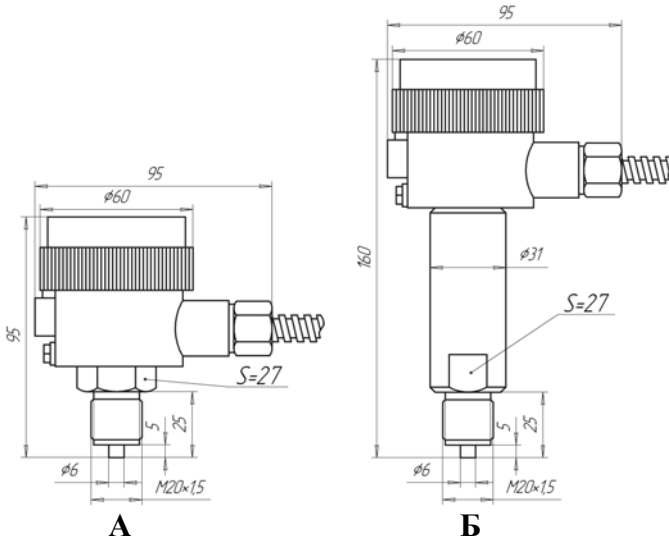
Модель 1200. Взрывозащита, нержавеющий корпус, встроенный кабель.
